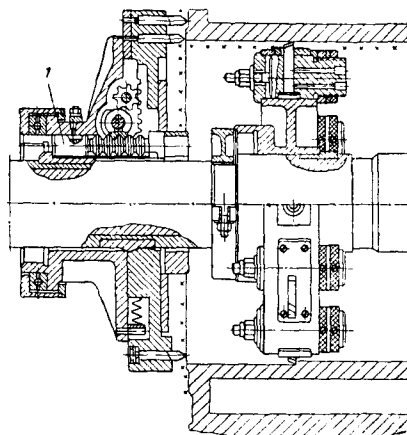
Специальный агрегат для обработки цилиндров паровозов
